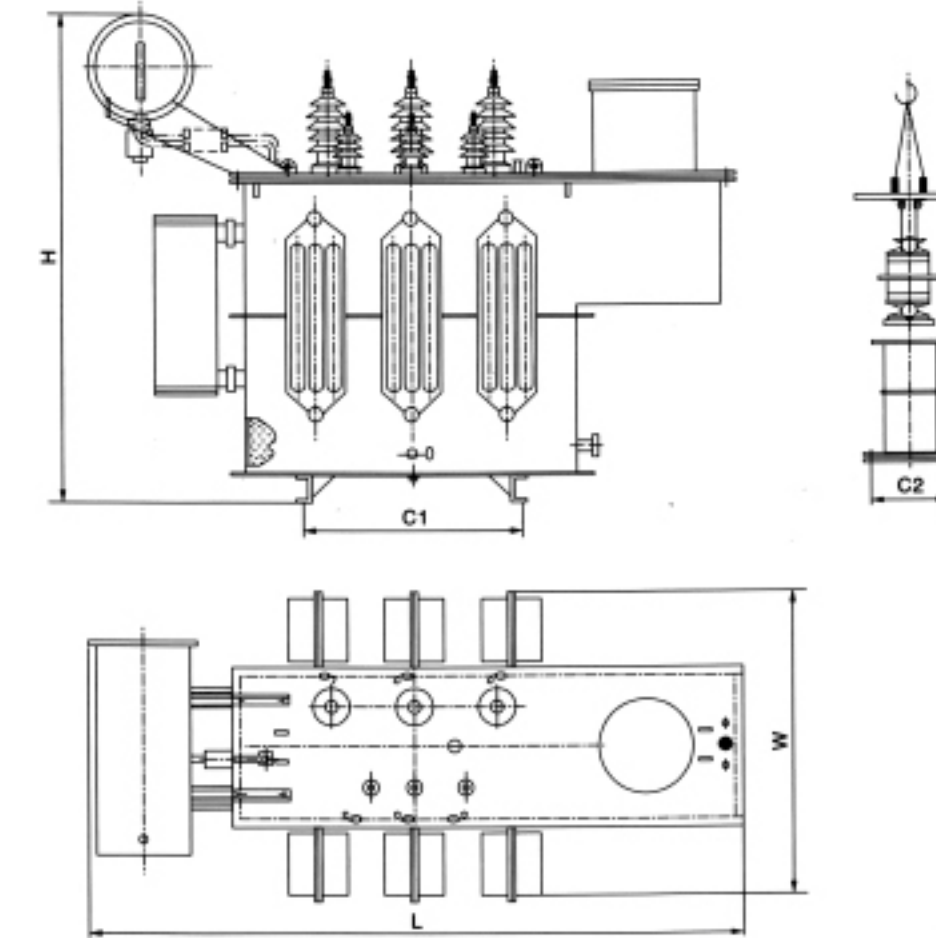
SZ9-800~31500/35变压器外形及安装尺寸
